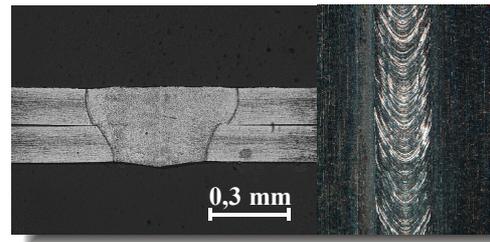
Querschliff und Oberraupe einer Überlappschweißung zweier 0,15 mm dicken Edelstahlbleche
